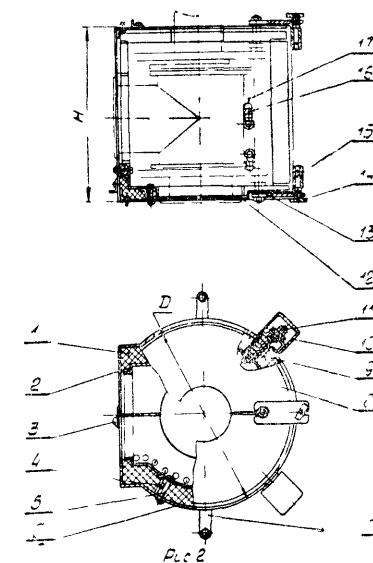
1 — теплоизолятор; 2 — экран; 3 — защелка; 4 — упор, 5 — винт; 6 — кожух наружный; 7 — ручка; 8 — крышка верхняя, 9 — втулка, 10 — колпак; 11 — клемма; 12 — крышка нижняя; 13 — планка; 14 — гайка; 15 — ось, 16 — бусы чешуйчатые; 17 — нагреватель.
